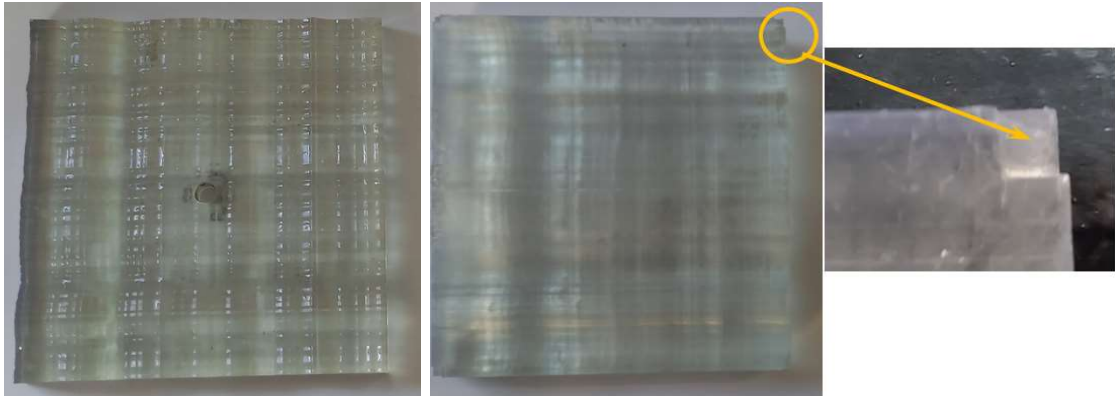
Detalle de orificio superior en piezas tipo B y detalle de muesca (tipo A)
